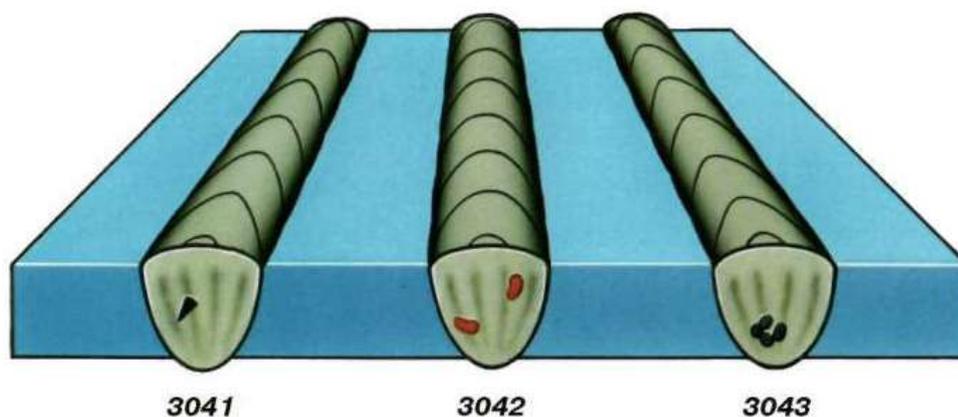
Дефект сварного шва по типу наличия металлических включений
